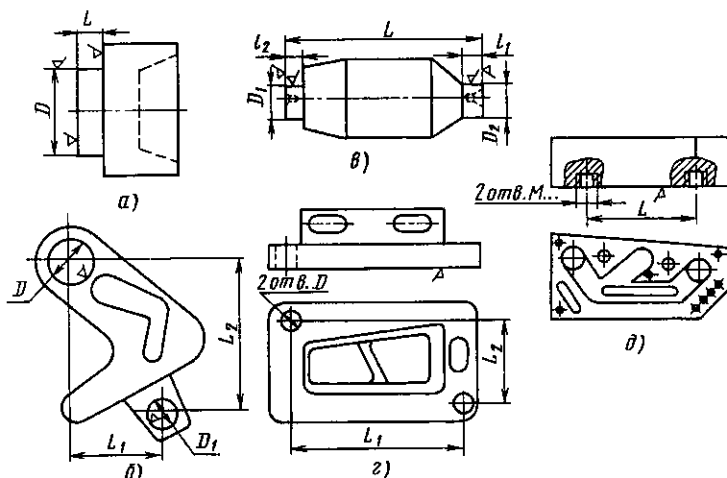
Примеры заготовок с базовыми поверхностями, подготовленными для обработки на станках с ЧПУ
